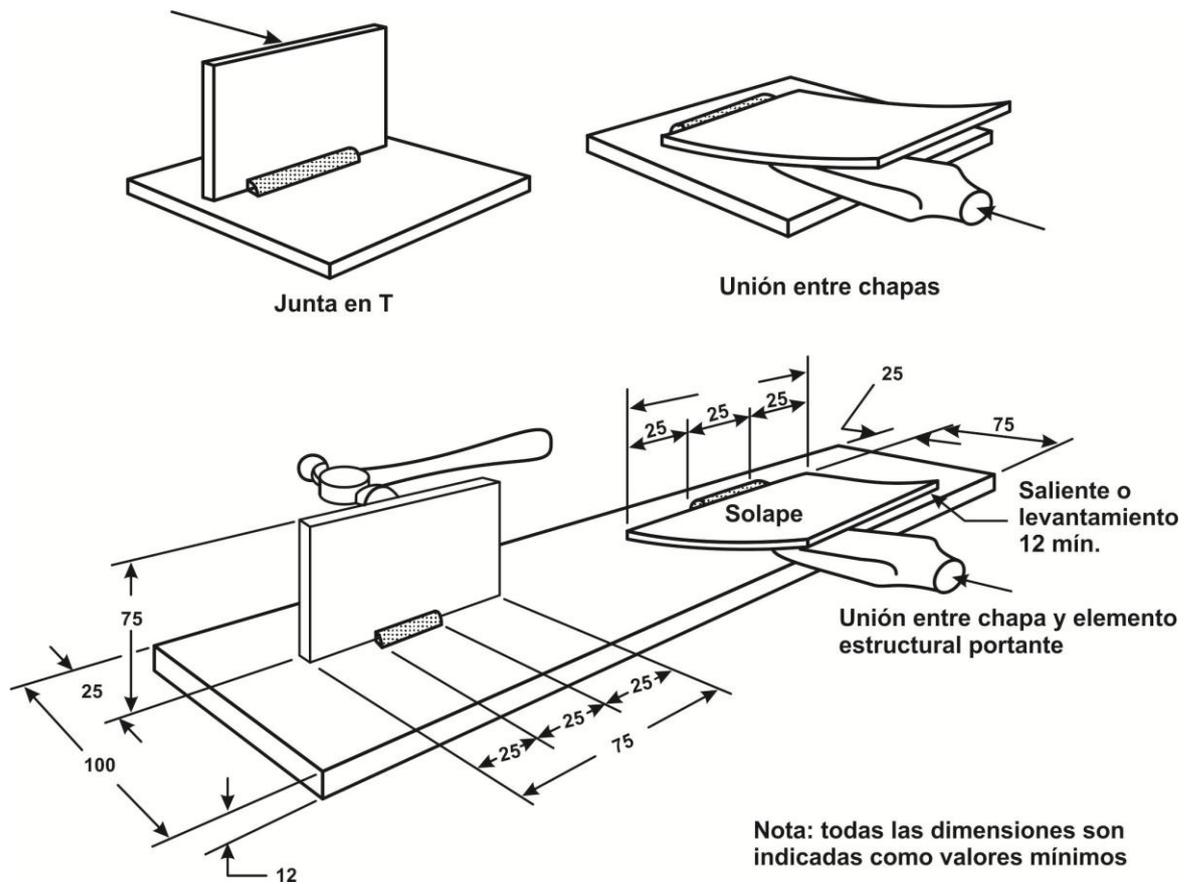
a). Esquema de ensayo para soldaduras de filete.
